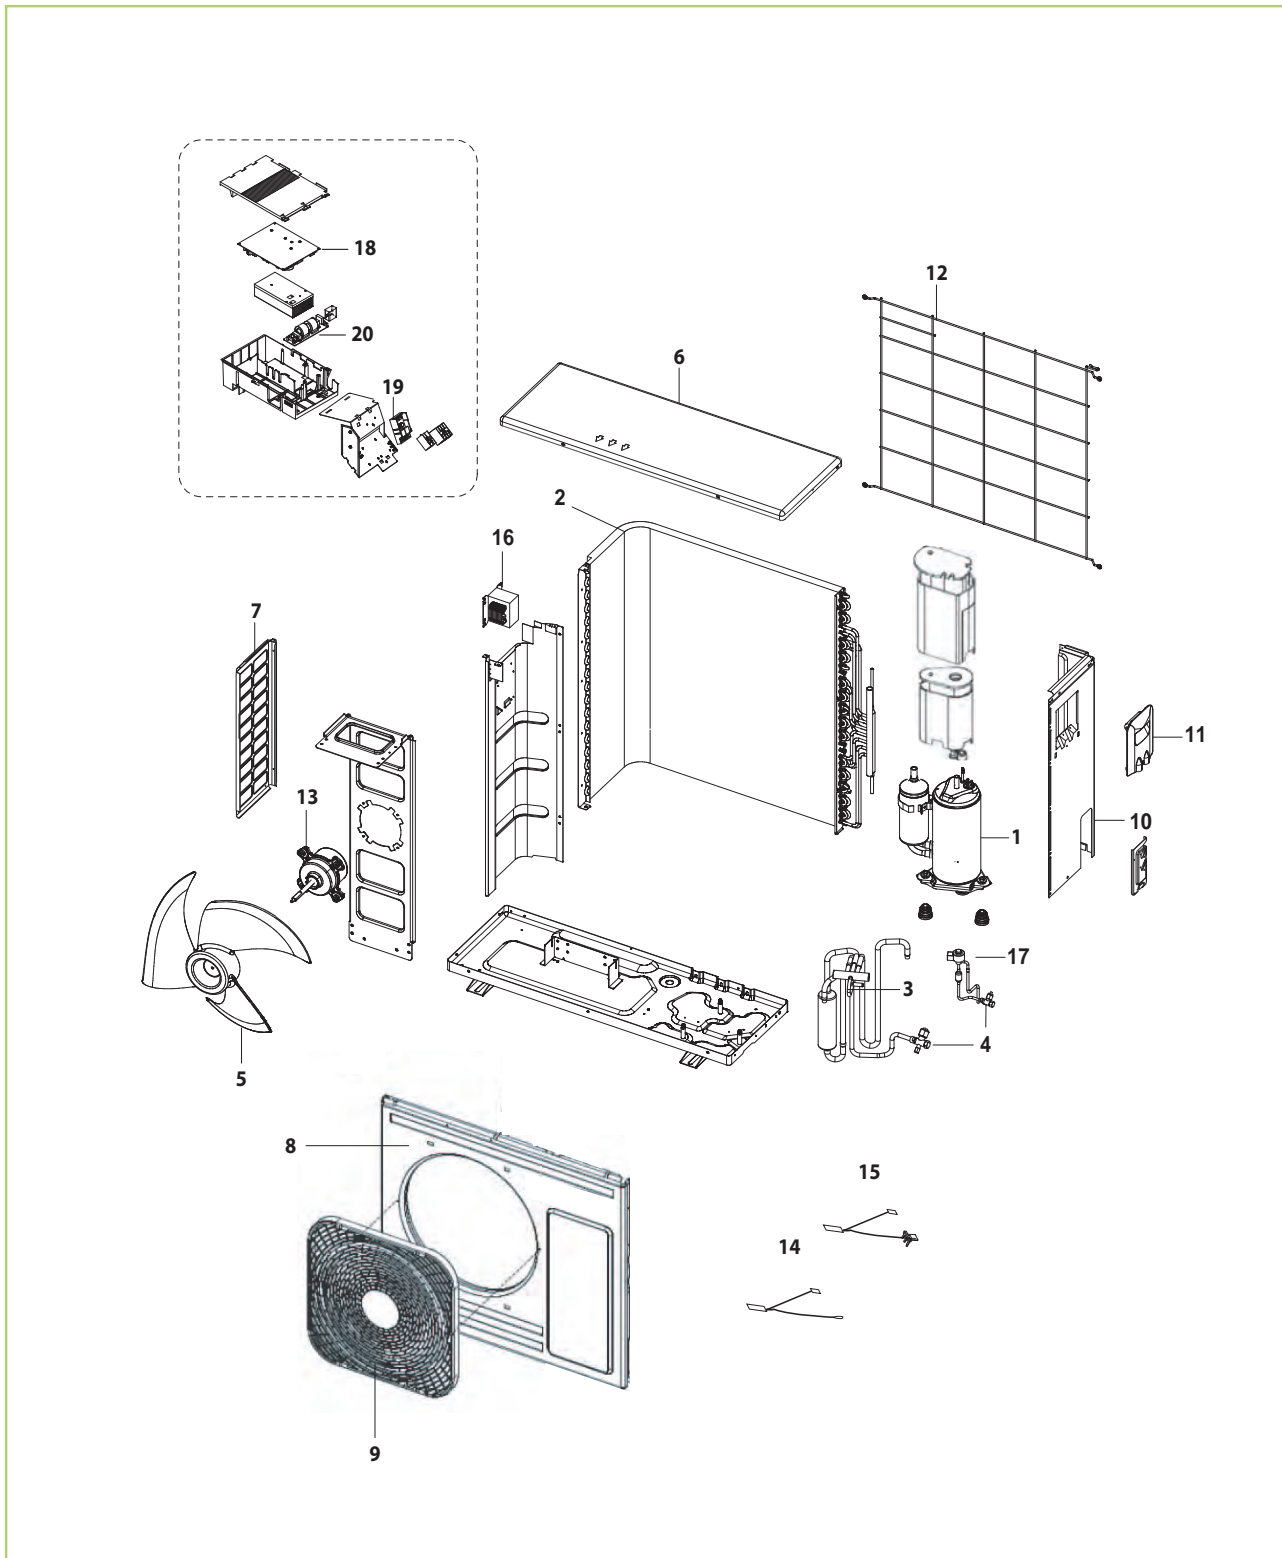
Explosionszeichnung Außenmodul WKF/WKF-compact 85
